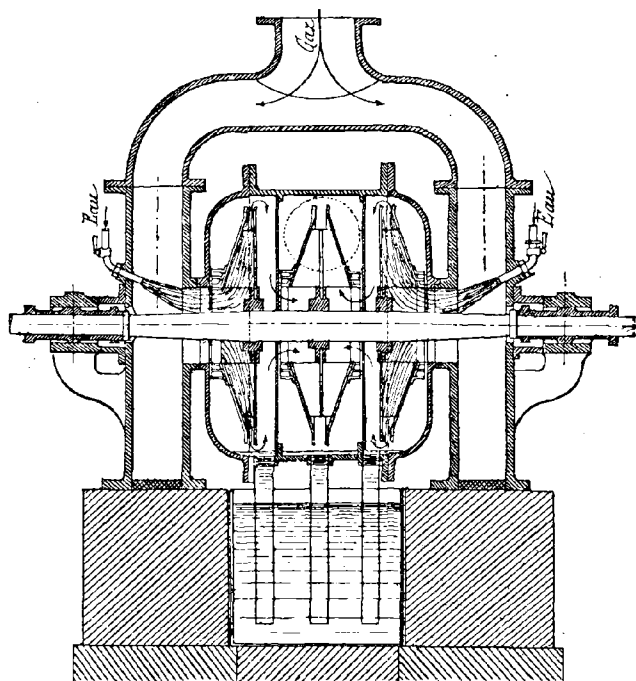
Ventilateur-épurateur, type Lencauchez.
